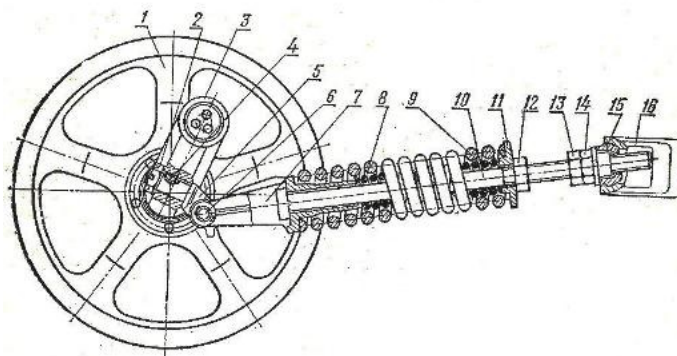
Направляющее колесо и натяжной механизм ДТ-75
